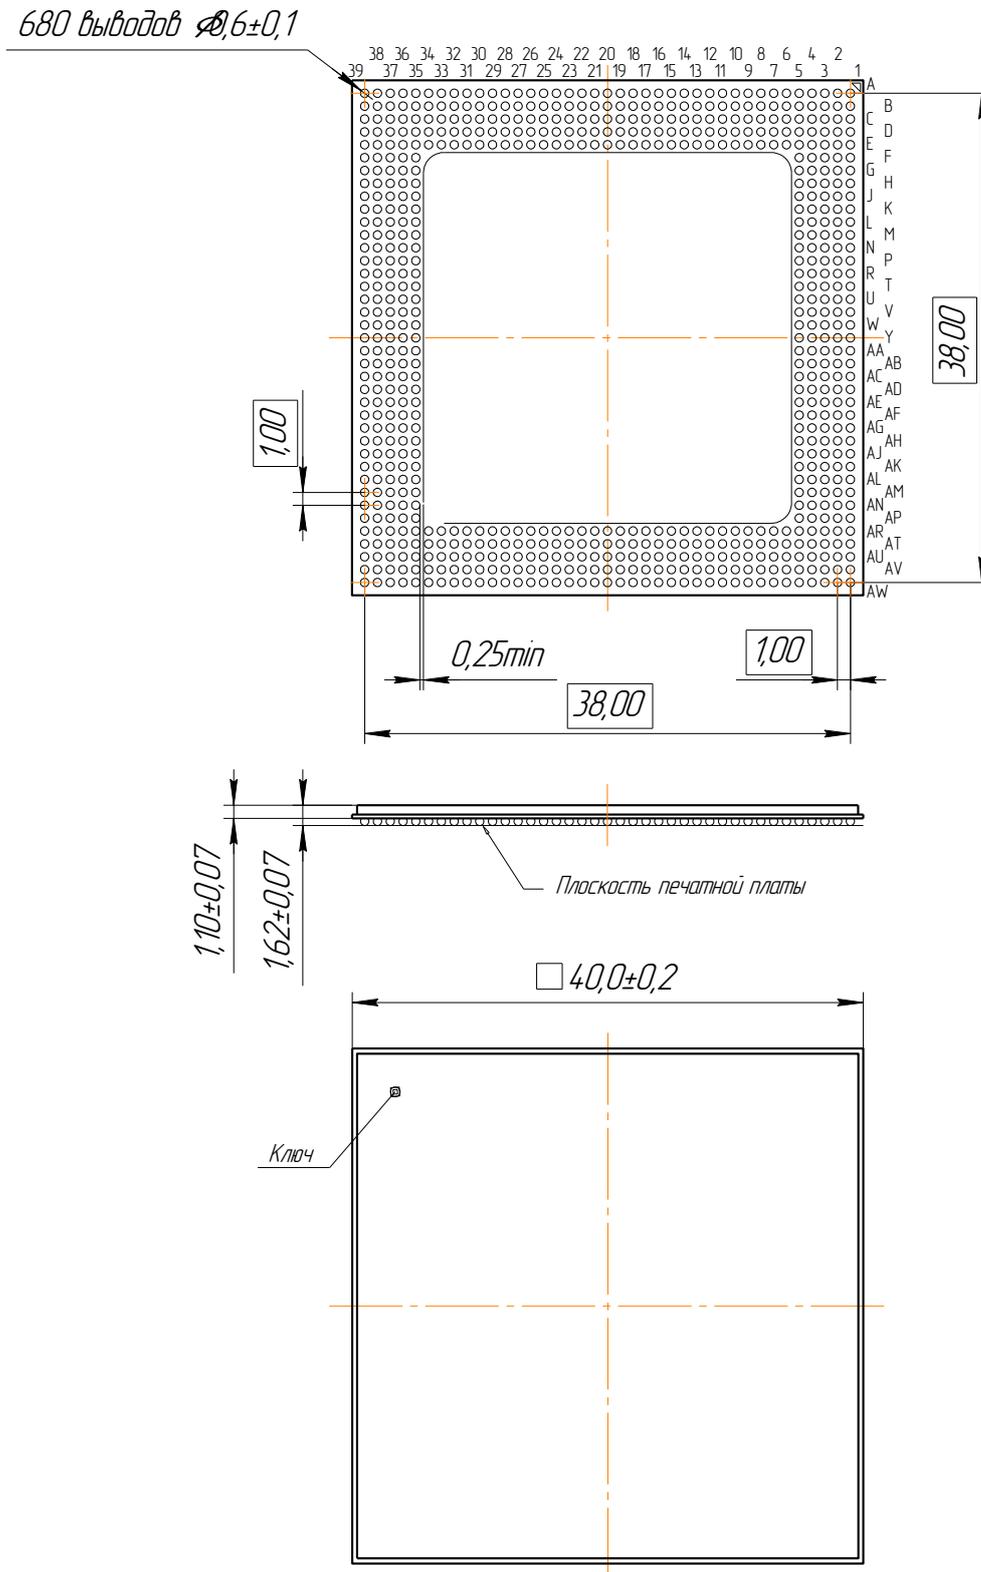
Чертеж корпуса 6304.680-1
